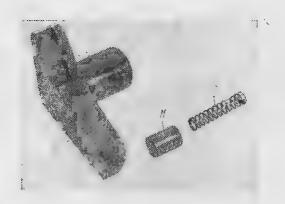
Предохранительный механизм: 8 — пружина 2A20.02-35; 11 — колпачок 2A20.02-88; 12 — предохранитель спуска 2A20.02-4
